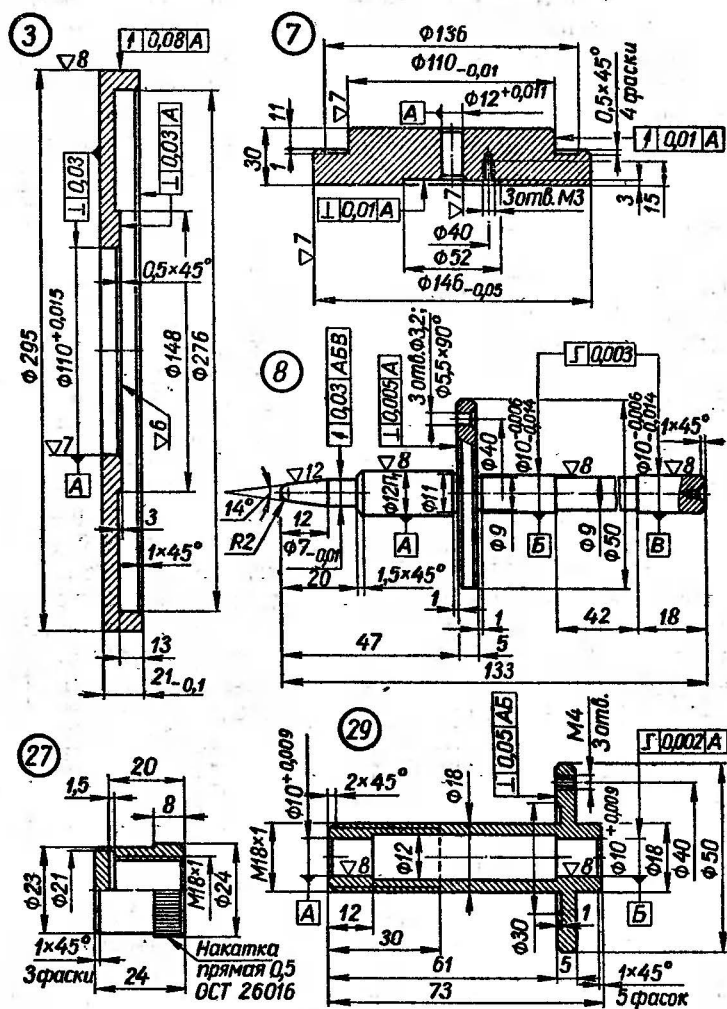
Детали узла диска проигрывателя: 3 — диск, Д16-Т, полировать; 7 — шкив-маховик, Д16-Т, оксидировать; 8 — валик проигрывателя, Ст. 40Х, калий НРС 42...44; 27 — гайка, Бр.АЖ9-4, оксидировать; 29 — втулка, Бр.АЖ9-4, оксидировать, кроме отверстий диаметром 10 мм
